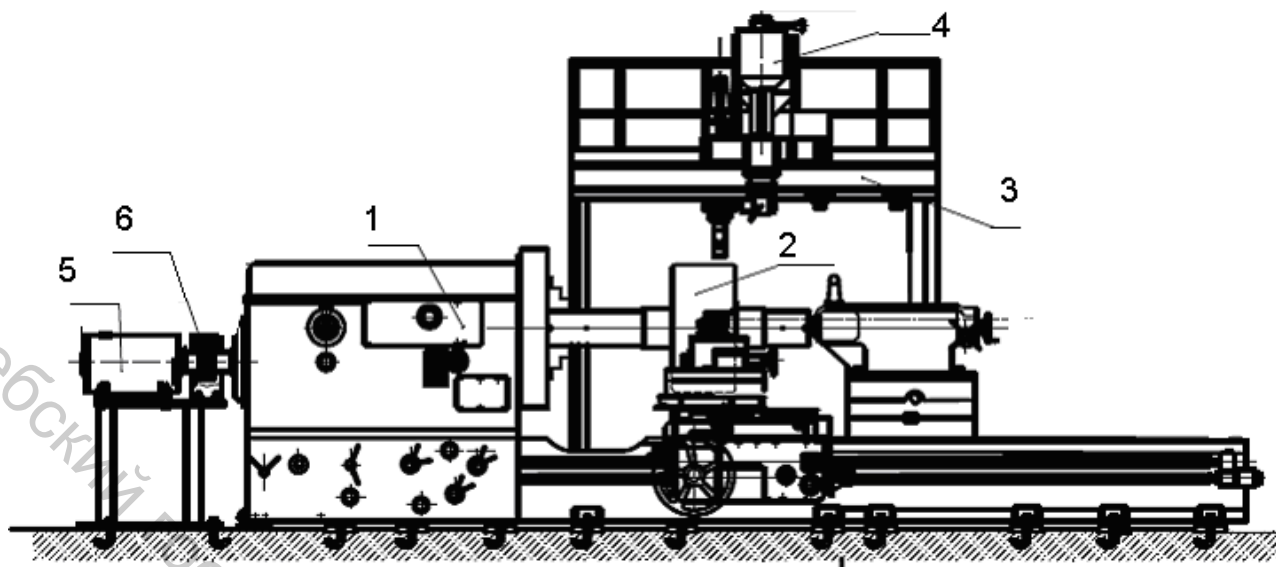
Установка для восстановления рабочей поверхности роликов
